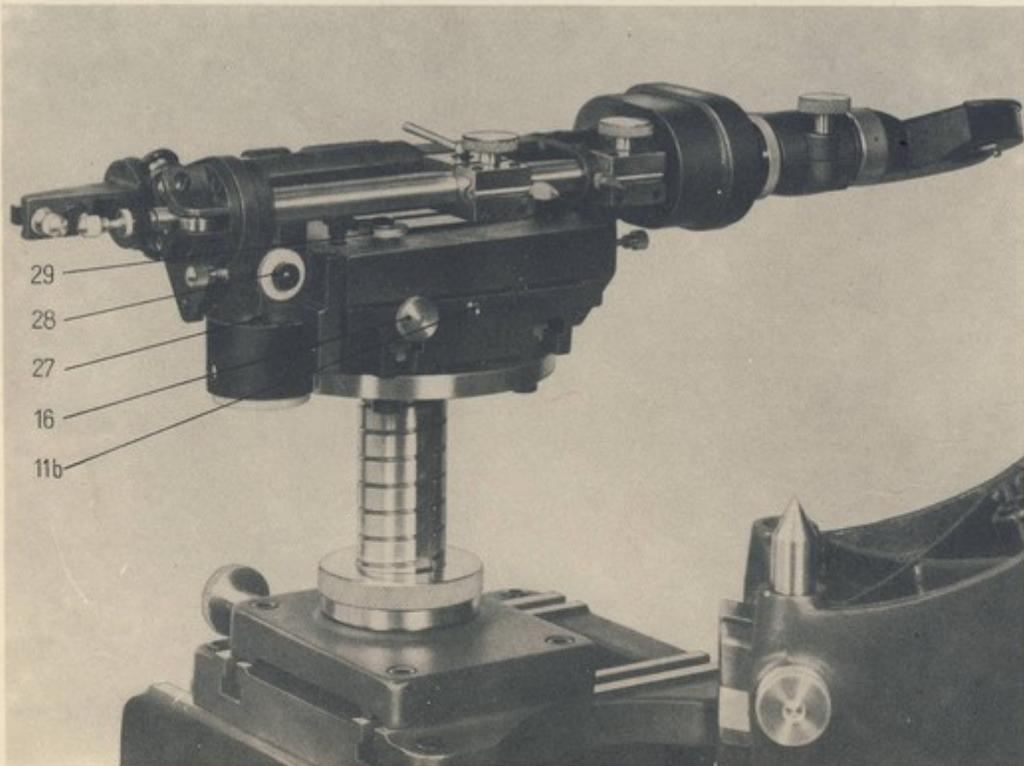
Meßeinrichtung; Gewichtszug eingehängt, Meßschnäbel eingespant.
